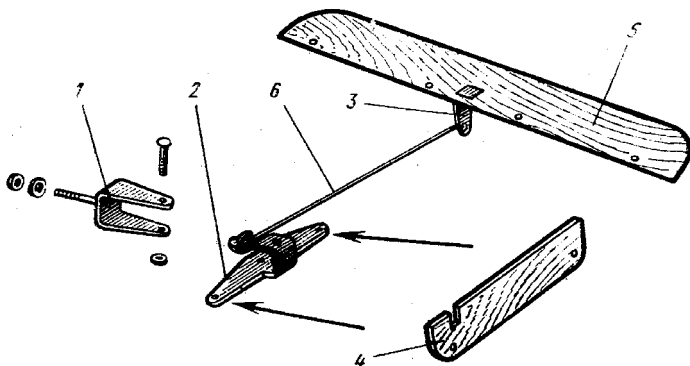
Компонировка деталей механизма управления рулем высоты:
